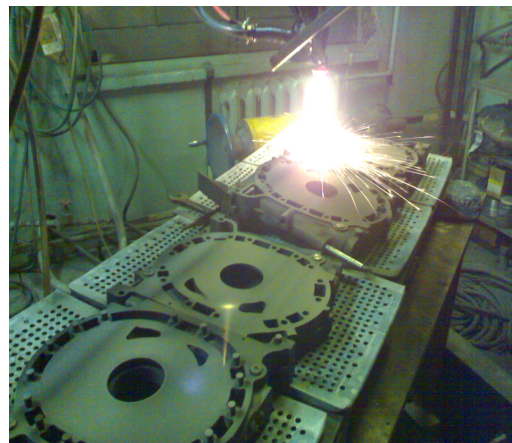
Восстановление рабочей поверхности корпусных деталей (крышек) роторно-поршневых двигателей «Mazda»
